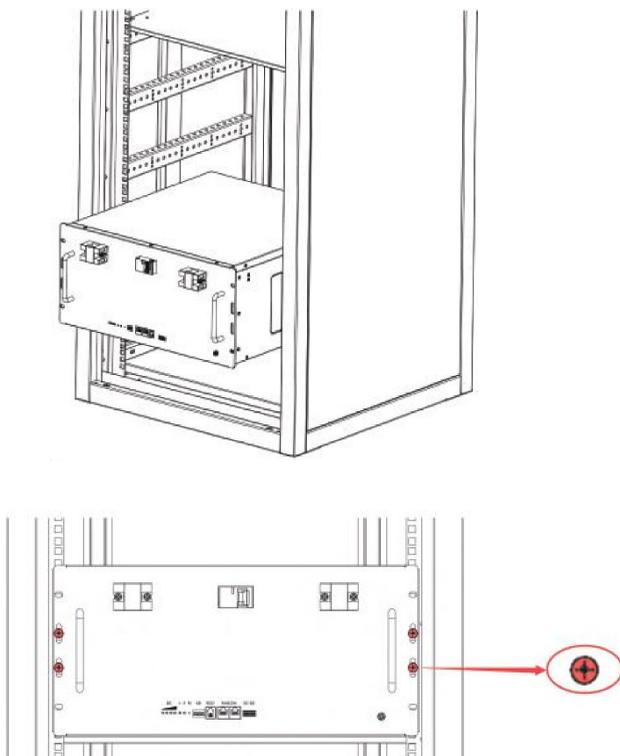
Fissare la batteria sul cabinet o sul rack
